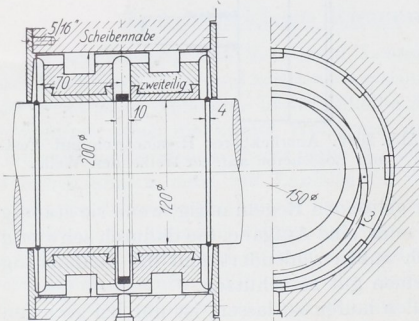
Leerlaufbüchse mit Ringschmierung. Prager Maschinenbau-A. G. M. 1:5.
